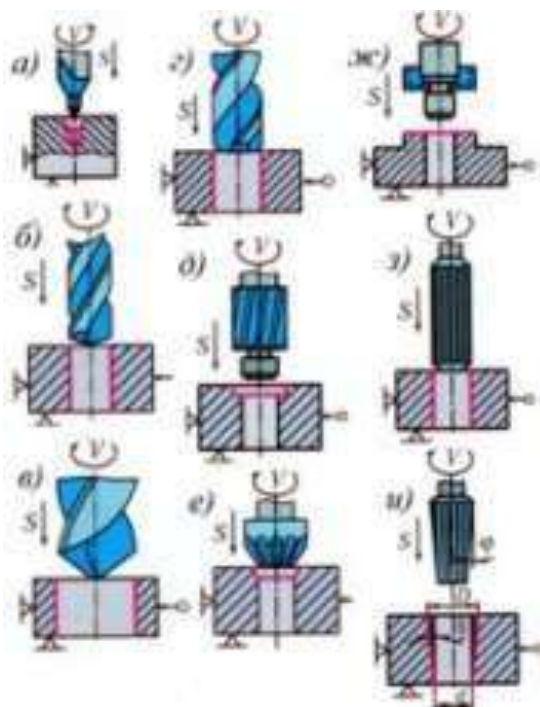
Обработка отверстий на вертикально-сверлильном станке
